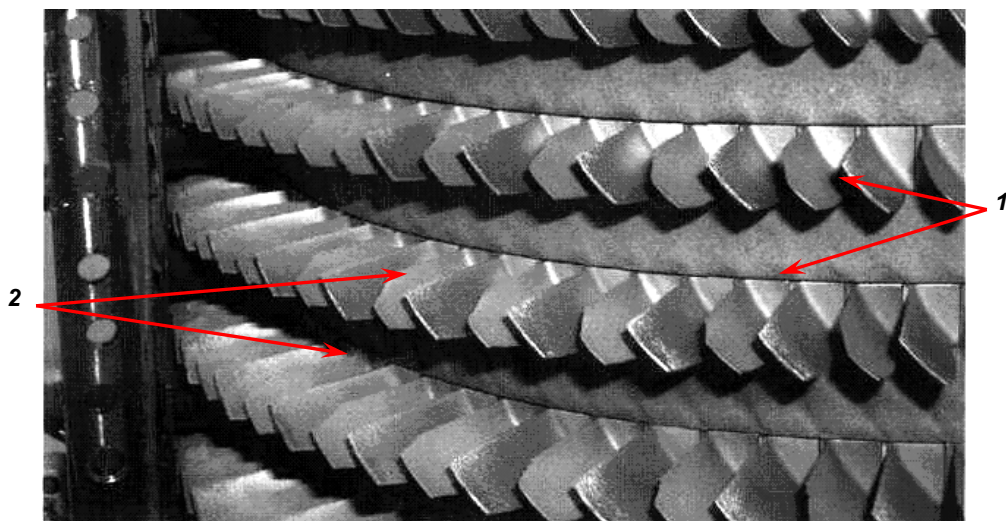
Ротор компрессора вертолетного двигателя после испытаний на эрозийный износ лопаток [8]:
